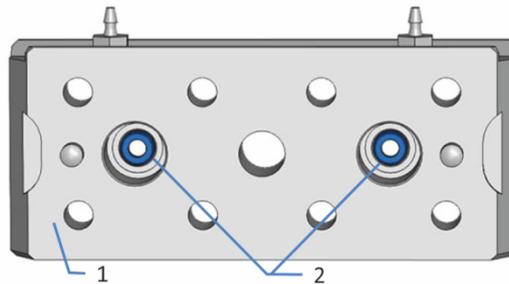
Plaque de rinçage des joints (côté opposé à la voie)
